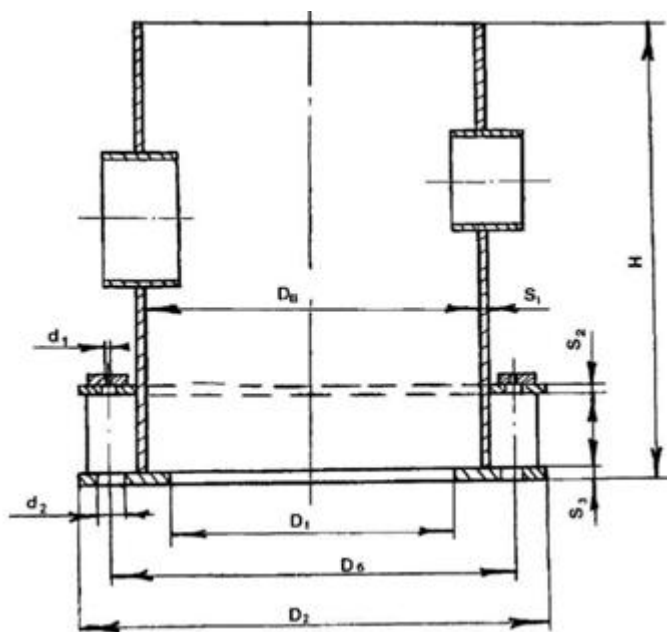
Розрахункова схема циліндричної опори для колонного апарата
